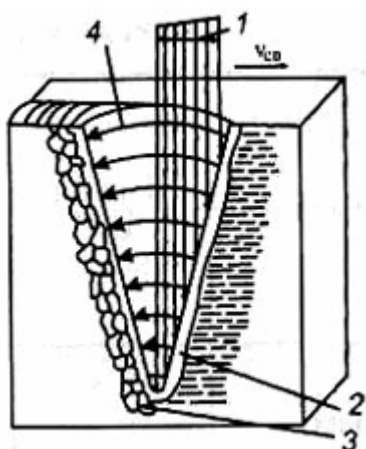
Образование сварного соединения при электронно-лучевой сварке: 1 – электронный луч; 2 – передняя стенка кратера; 3 – зона кристаллизации; 4 – путь движения жидкого металла
